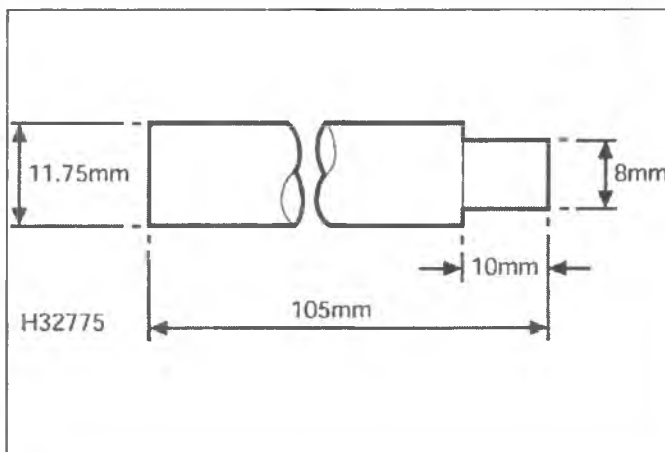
,а. Размеры блокирующего стержня коленчатого вала
